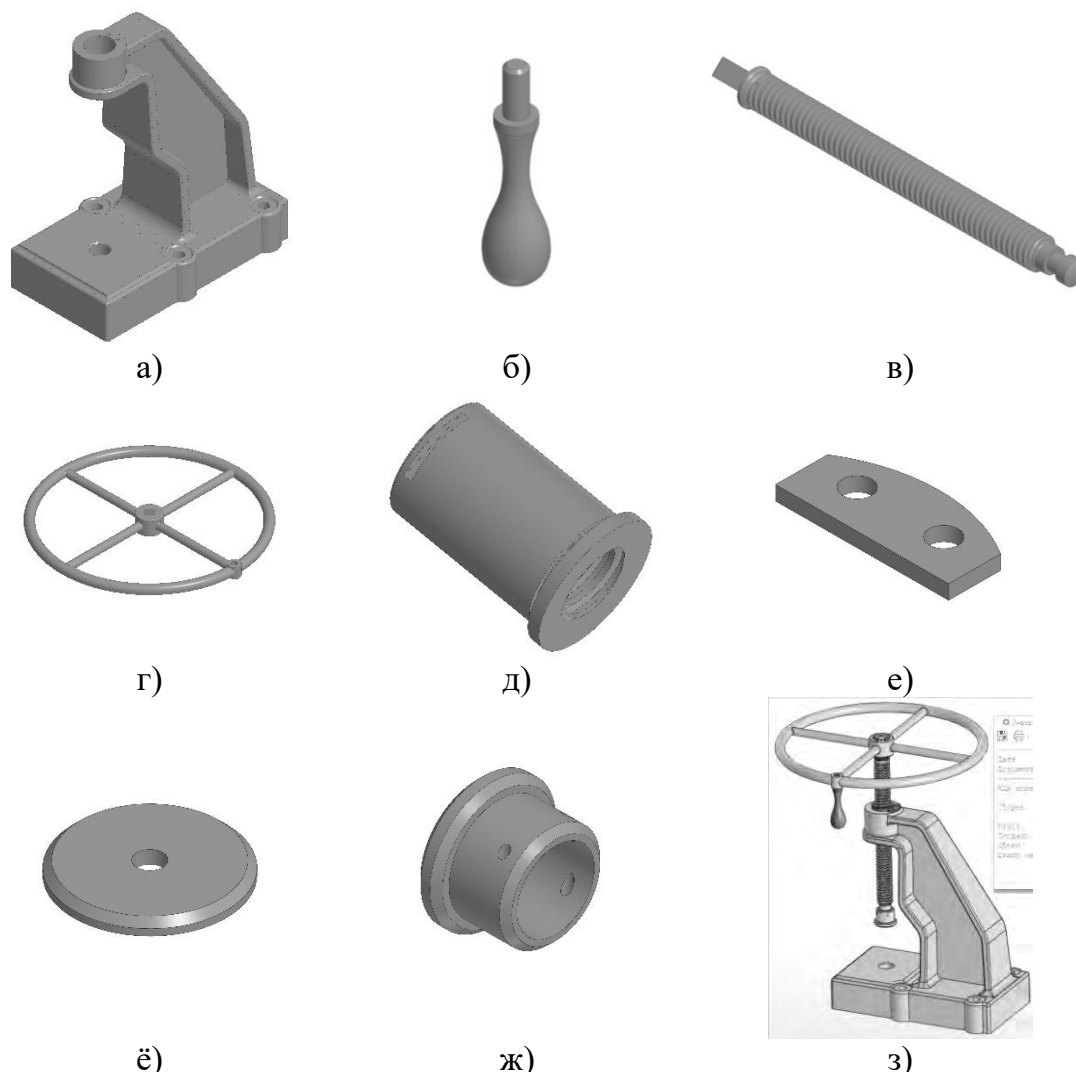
Детали ручного пресса в Компас-3D: а) станина, б) рукоятка, в) винт, г) маховик, д) гайка, е) планка, ё) шайба, ж) колодка, з) общий, сборочный чертёж ручного пресса
